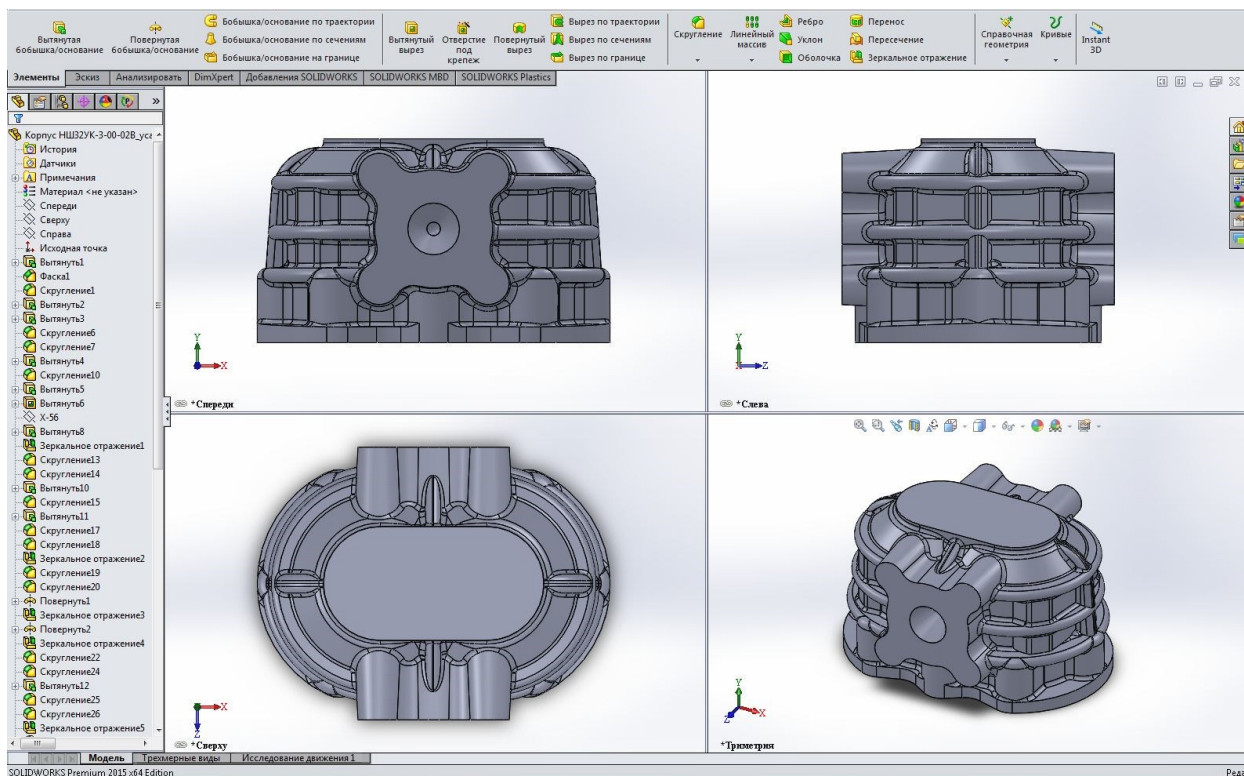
3D-модель виливка «Корпус НШ32УК»
